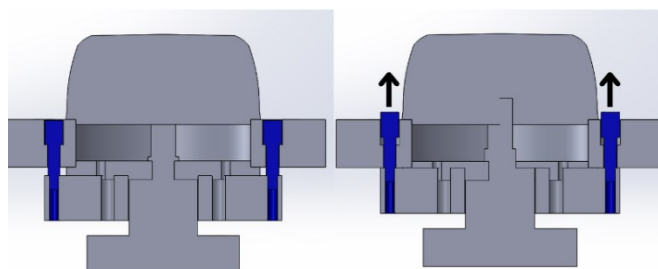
Desenho esquemático do molde desenvolvido para a fabricação da Panela 16
